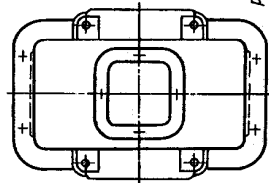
Цельнолитой корпус зубчатого цилиндрического редуктора без развема
